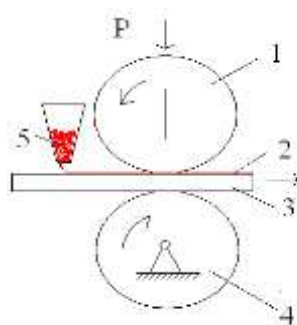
Схема приспособления для плакирования поверхности твердосплавным порошком: 1 Прижимной ролик; 2. Слой твердосплавного порошка; 3. Лемех. 4. Подпорный ролик; 5. Бункер для порошка
